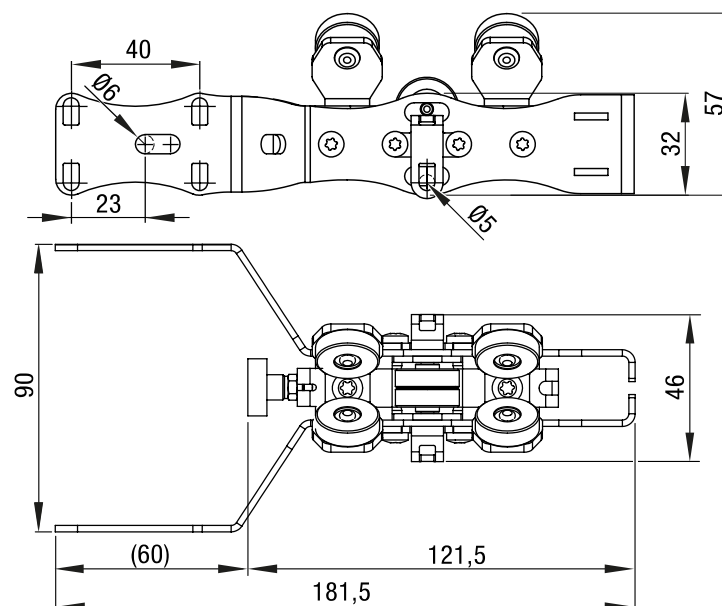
Maße – Zugwagen mit doppeltem Überzugbügel (OFFICE)
